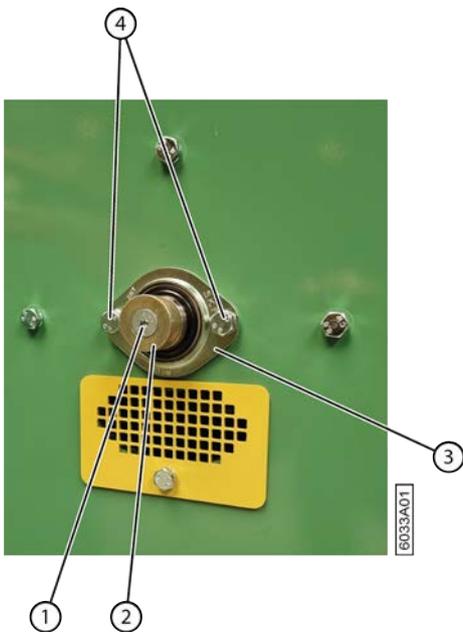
Remplacer le roulement de l'essieu du moulin (arrière)
